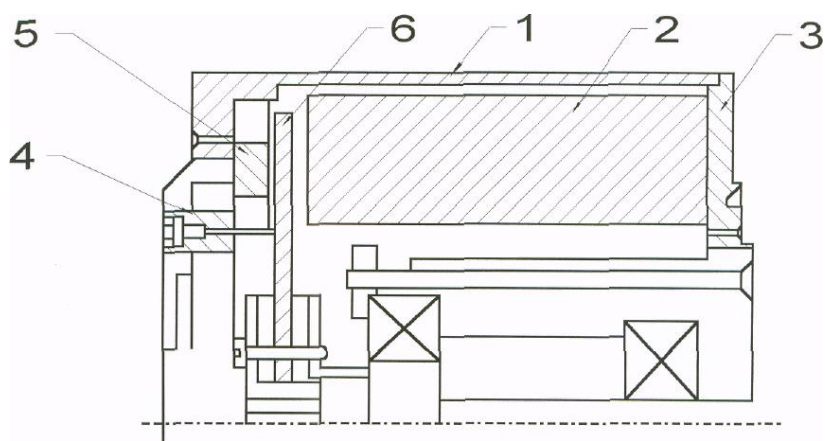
Высокмоментный двигатель постоянного тока
